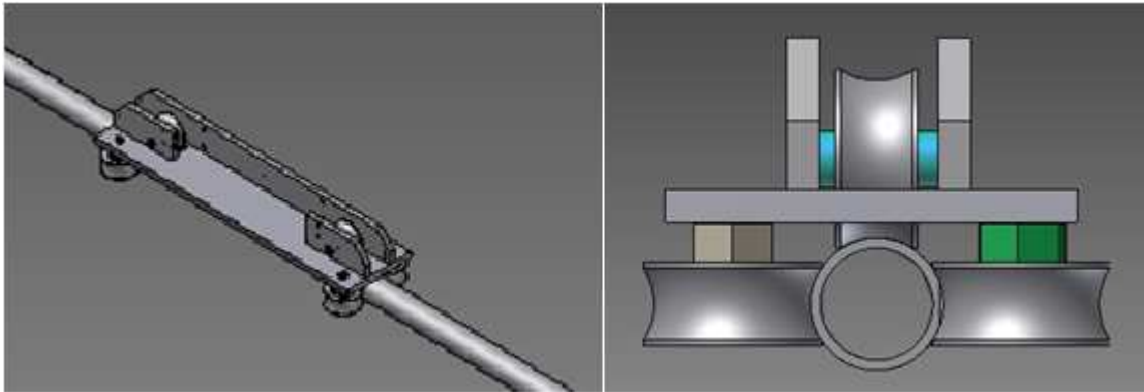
Conjunto de guía y deslizador a construir
